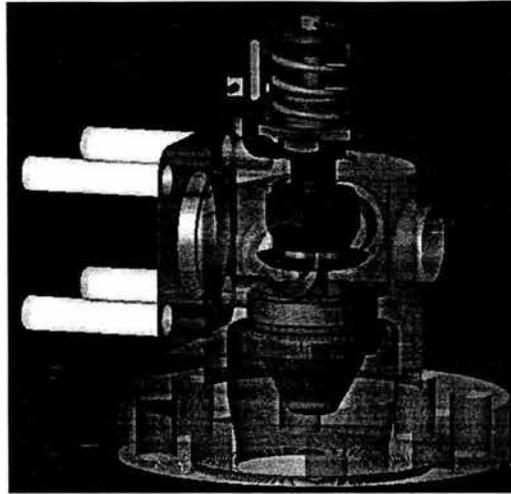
Vista en corte de la válvula de admisión de vapor del soplador de hollín.
